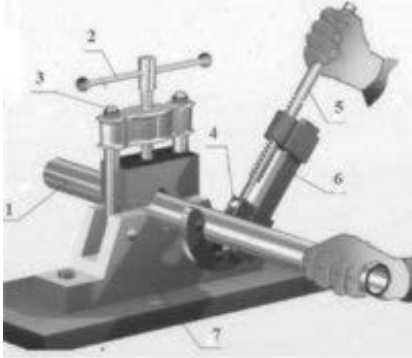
Труборіз: 1 – труба, 2 - рукоятка, 3 – гвинт, 4 – рухомий ролик, 5 – рукоятка труборіза, 6 – труборіз, 7 – притис
